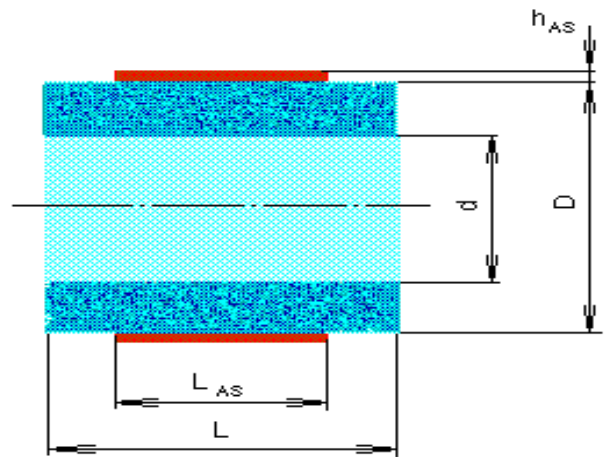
Verschleißteil mit zylindrischer Oberfläche - horizontale Bauteillage, Auftragschweißung außen.
